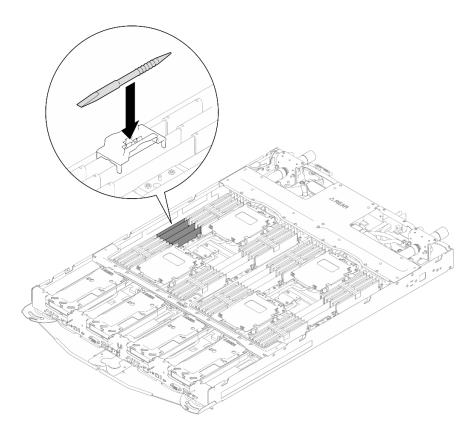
Befestigen des Speichermodul-Werkzeugs
